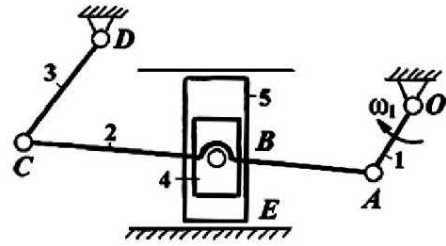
Механизм пресс-автомата с плавающим ползуном
